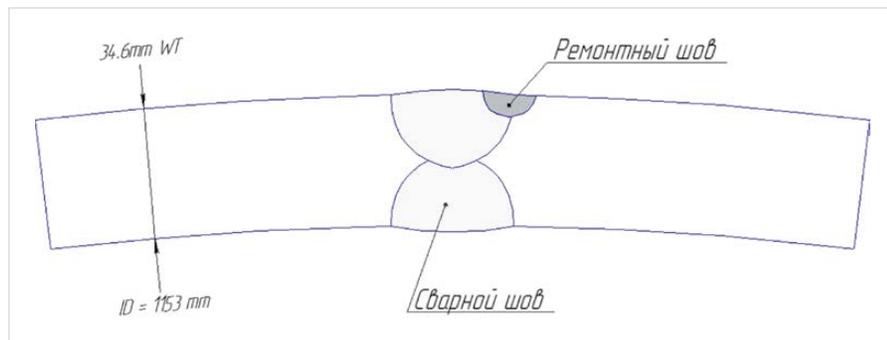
Полнотолщинный образец с моделированным участком ремонта сварного шва для испытаний методом четырехточечного изгиба
